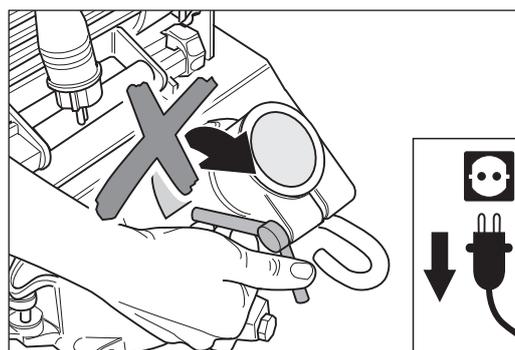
Bei ausgebautem Führungsrohr die Flügelmutter am Maschinengehäuse nicht fest anziehen!
